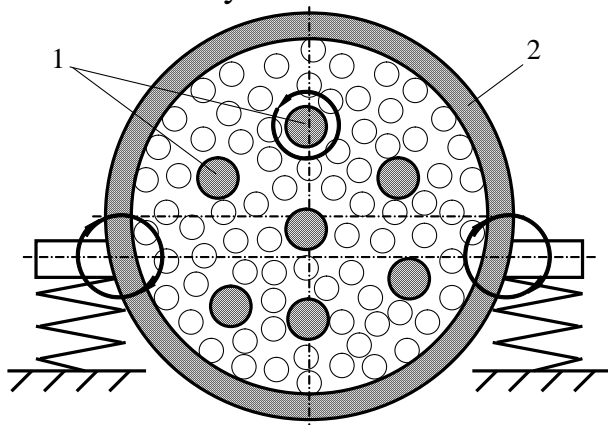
Принципова схема обробки поверхонь проволочок вільними кульками
